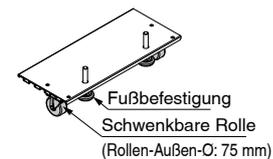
Laufrollen und einstellbare Fußbefestigung (2 Stk.)
